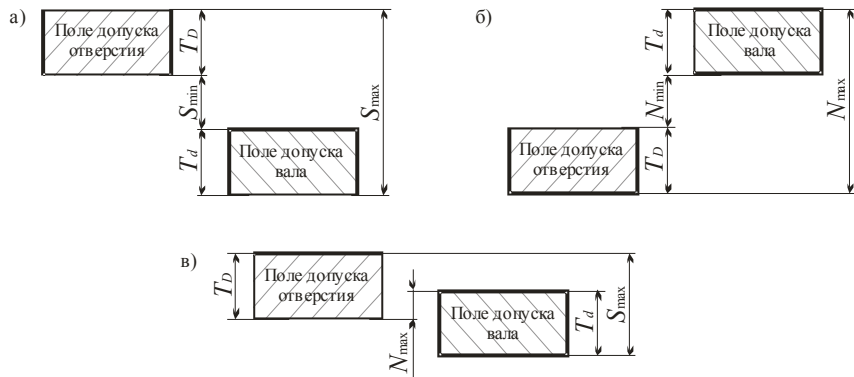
Схема расположения полей допусков отверстия и вала в посадках: а) с зазором; б) с натягом; в) переходных
